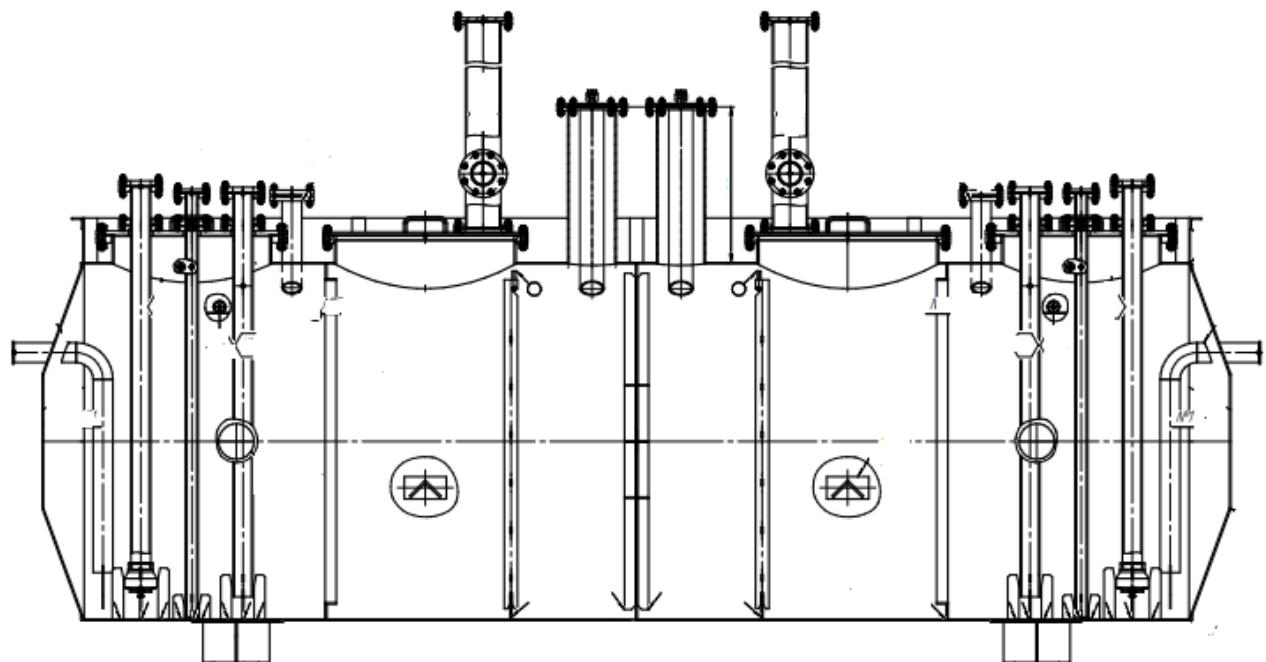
Эскиз резервуара горизонтального стального цилиндрического РГСП-10,
